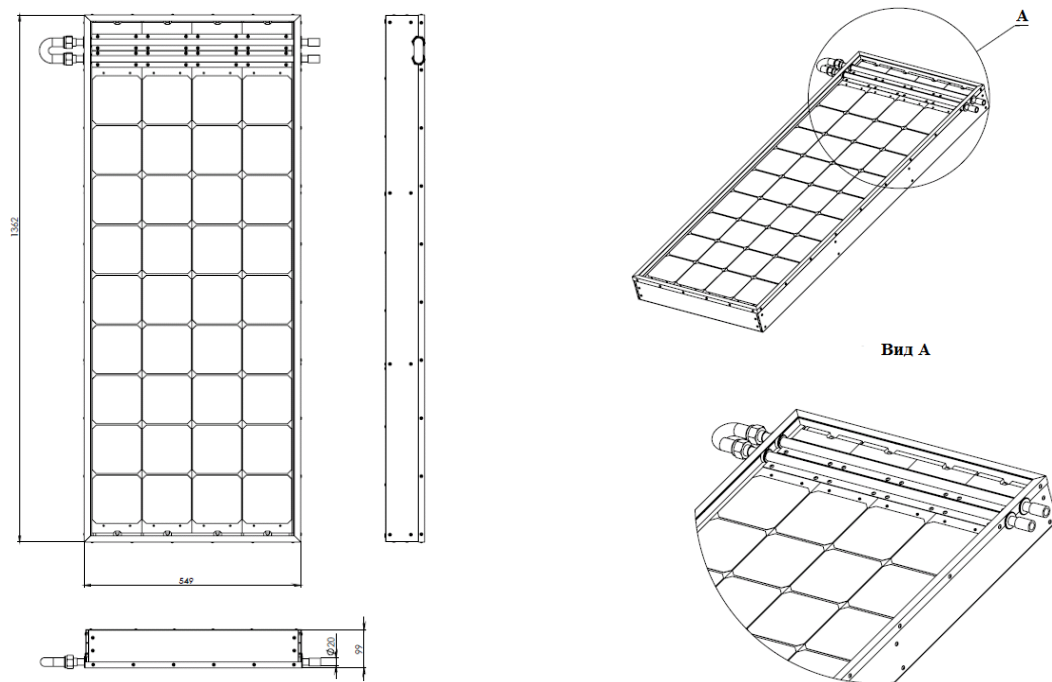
Ескіз конструкції зразка комбінованого сонячного колектора
